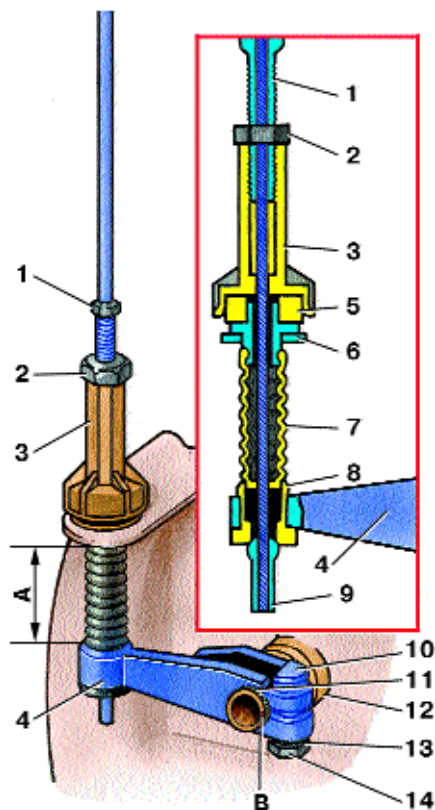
Регулировка привода выключения сцепления: 1 – наконечник оболочки троса привода выключения сцепления; 2 – контргайка; 3 – резьбовая втулка; 4 – наружный рычаг вала выключения сцепления; 5 – демпфер; 6 – кронштейн; 7 – защитный чехол; 8 – вкладыш; 9 – наконечник троса; 10 – болт; 11 – вал рычага выключения сцепления; 12 – втулка вала; 13 – шайба; 14 – гайка; В – метка на торце вала
